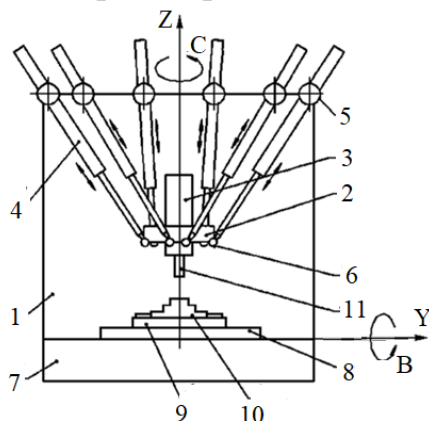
Схема гексапода: 1 – основание; 2 – подвижная платформа; 3 – шпиндельный узел; 4 – штанги; 5 – шарнир основания; 6 – шарнир платформы; 7 – станина; 8 – стол; 9 – приспособление; 10 – заготовка; 11 – инструмент
